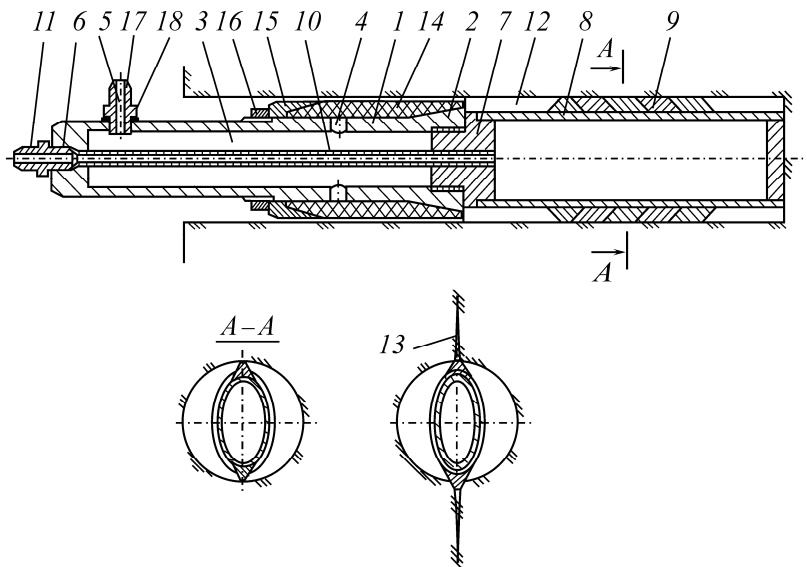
Устройство для создания иницирующей трещины вдоль скважины: 1 — корпус; 2 — конический выступ; 3 — центральный канал; 4 — радиальное отверстие; 5 — отверстие; 6 — отверстие; 7 — переходная втулка; 8 — камера; 9 — клинья; 10 — трубка; 11 — штуцер; 12 — скважина; 13 — иницирующая трещина; 14 — эластичная трубка; 15 — втулка; 16 — гайка; 17 — втулка; 18 — прокладка
